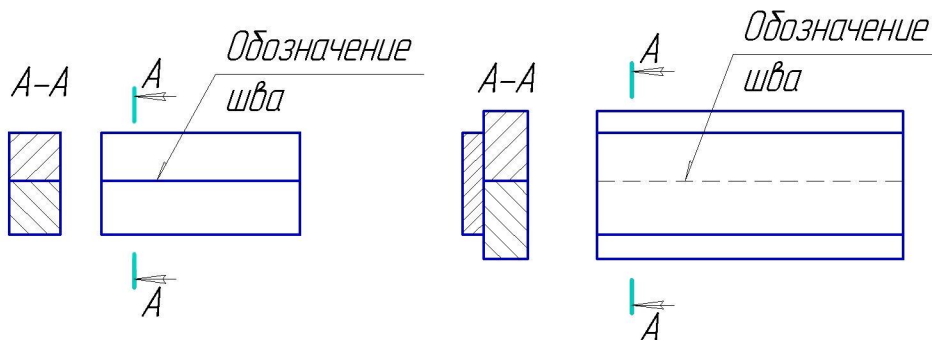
Изображение сварных швов на чертеже.
